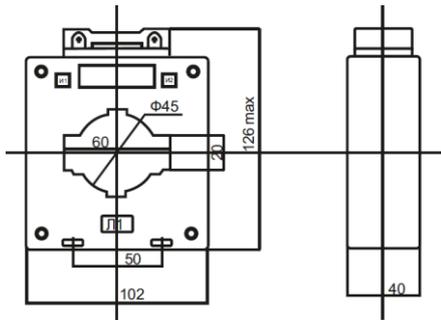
Габаритные и установочные размеры трансформаторов тока ТШП-0,66-60
